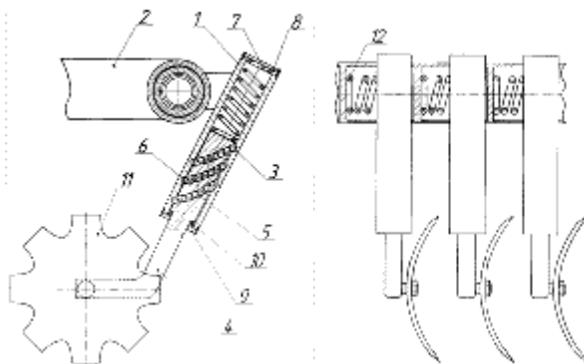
Предохранительное устройство почвообрабатывающего орудия:
